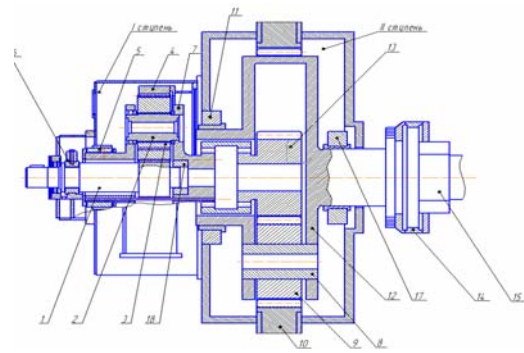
Планетарный редуктор предлагаемой конструкции (2 вариант): 1 - вал-шестерня I ступени; 2,8 - ось сателлита; 3,9 - сателлит; 4,10 - зубчатый венец; 5,11,16,17 - подшипники скольжения водила; 6 - подшипники скольжения вала-шестерни I ступени; 7,12 - водило; 13 - солнечная шестерня II ступени; 14 - зубчатая муфта; 15 - промвал; 18 - подшипник скольжения (втулка вала-шестерни)
